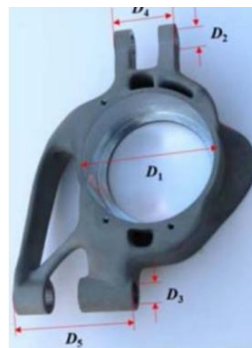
12. Mangueta manufacturada mediante manufactura aditiva de metal [21].
